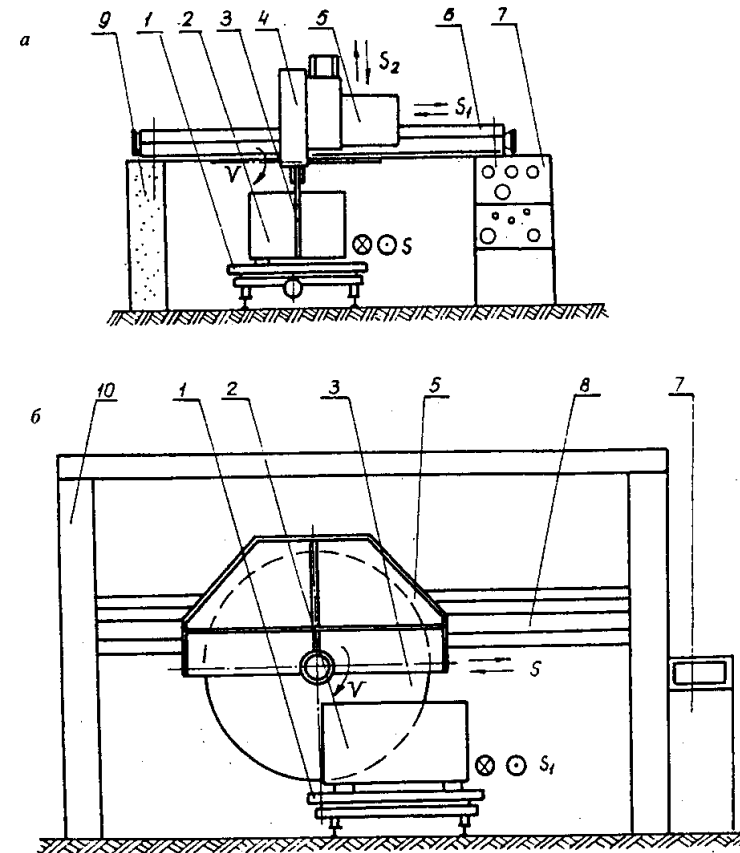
Схемы порталного и мостового однодисковых станков: а — порталный; б — мостовой; 1 — тележка; 2 — распиливаемый блок; 3 — алмазный отрезной сегментный круг; 4 — режущая головка; 5 — суппорт; 6 — траверса портала; 7 — пульт управления; 8 — мост; 9 — железобетонные опоры; 10 — колонны; V — окружная частота вращения АОСК (движение резания); S — рабочая подача (скорость перемещения отрезного круга); S₁ — установочное перемещение блока или инструмента (определяет толщину выпиливаемого изделия); S₂ — установочное движение отрезного круга, определяющее глубину врезания инструмента в блок (для твердых пород)
